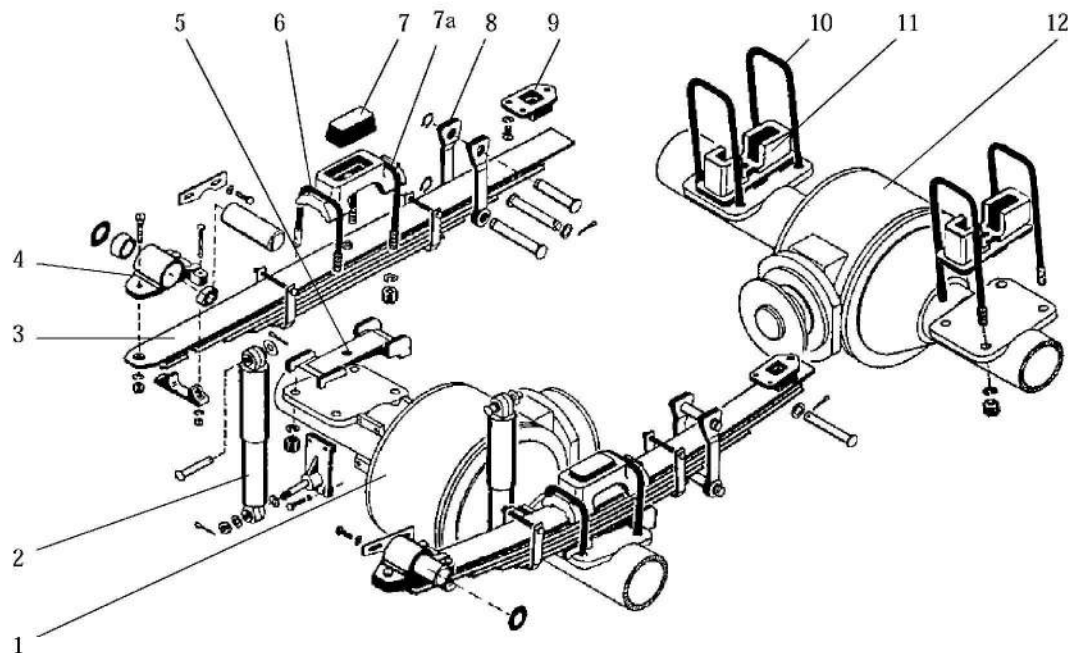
Подвеска ходовой системы: 1 – мост передний; 2 – амортизатор гидравлический; 3 – рессора полуэллиптическая; 4 – передний кронштейн рессоры; 5 – проставка переднего моста; 6 – стремянка рессоры; 7 – буфер; 7а – накладка; 8 – серьга; 9 – упор; 10 – стремянка балки заднего моста; 11 – проставка заднего моста; 12 – мост задний.
